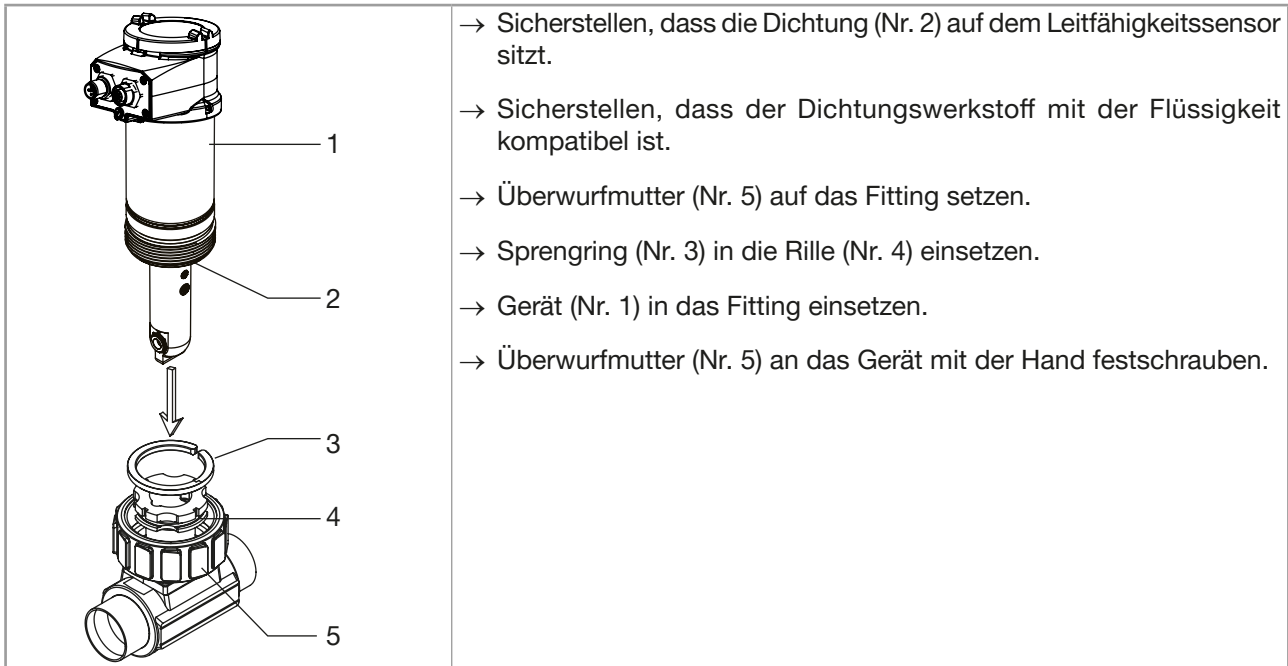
Installation einer Gerätevariante mit G2"-Überwurfmutter in ein Fitting Typ S020
